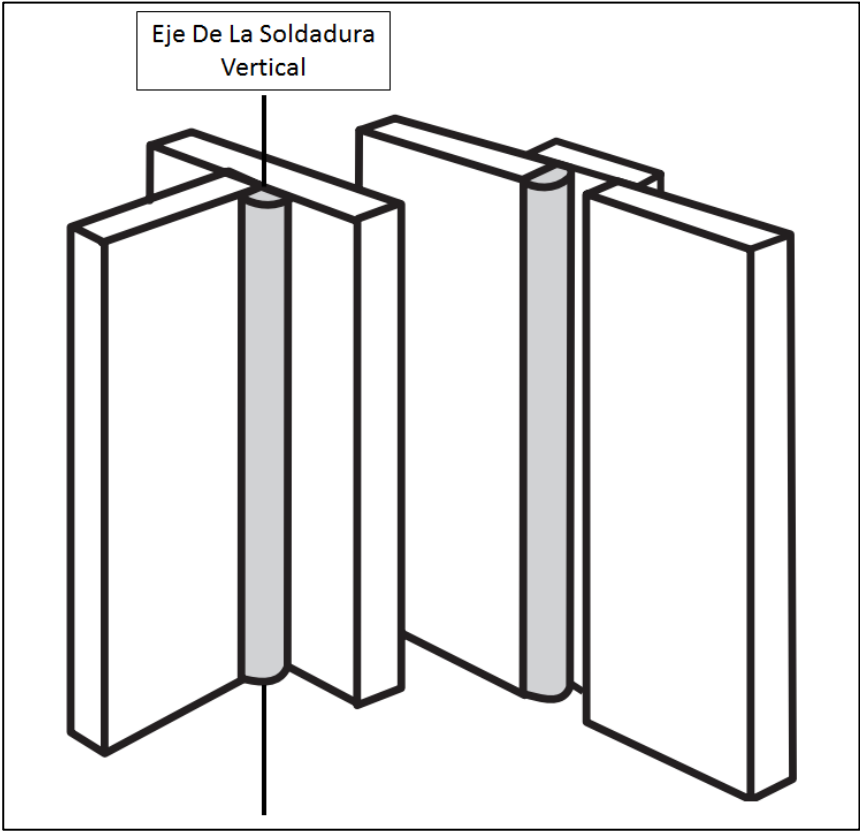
Soldadura De Filete En Posición 3F [58].
